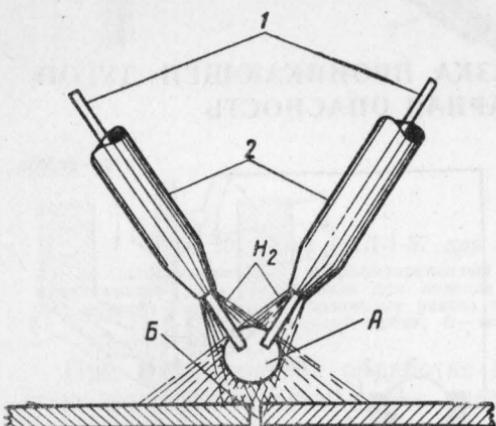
Схема процесса атомно-водородной сварки
